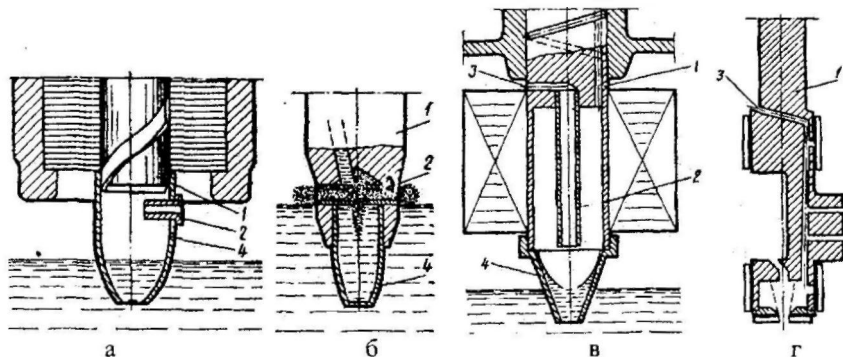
Устройства для удаления пара из смазочного масла:
